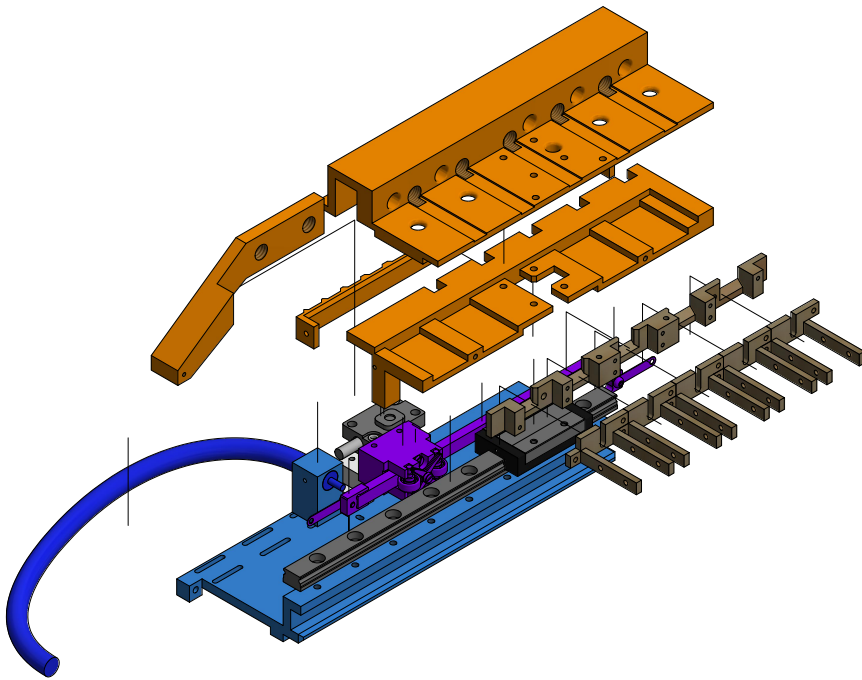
Explosionsansicht der Mechanik des primären Targets. Der Schlitten ist orange eingefärbt, die Befestigung der Motoren über Befestigungsschuh und Adapter dunkelgrau. Angetrieben wird dieser Aufbau vom violett eingefärbten Motor. Zusätzlich lassen sich der Encoder (grau) und der Lichtwellenleiter (dunkelblau) des selbst entwickelten Lagekontrollsystems erkennen.
